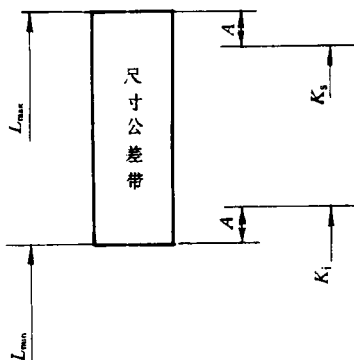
工件尺寸公差带及内缩方式的验收极限
